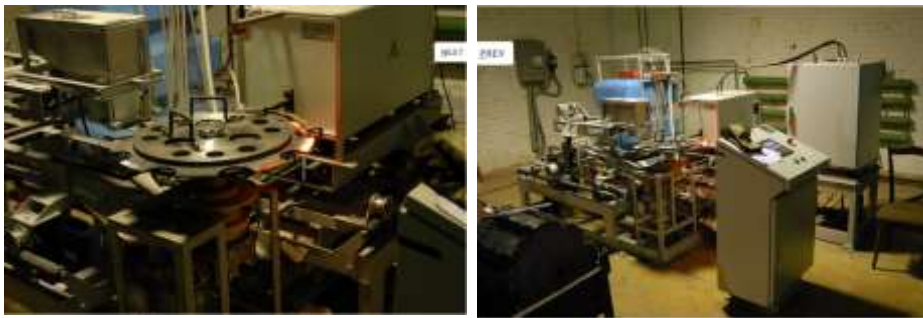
Установка для наплавки порошковых материалов ТВЧ
